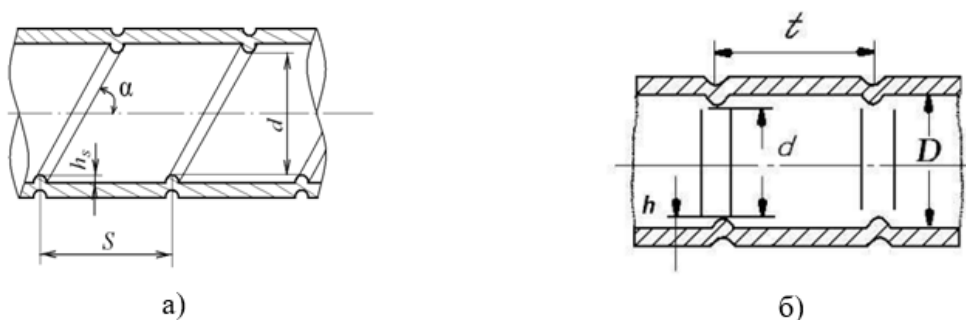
Схема винтовой накатки (а) и поперечной кольцевой накатки (б)
